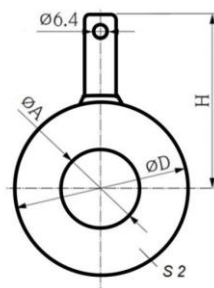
Габаритные размеры заземляющих дисков (колец) для фланцевых соединений с Ду от 700 мм (А, D, Н – размеры для справок)
